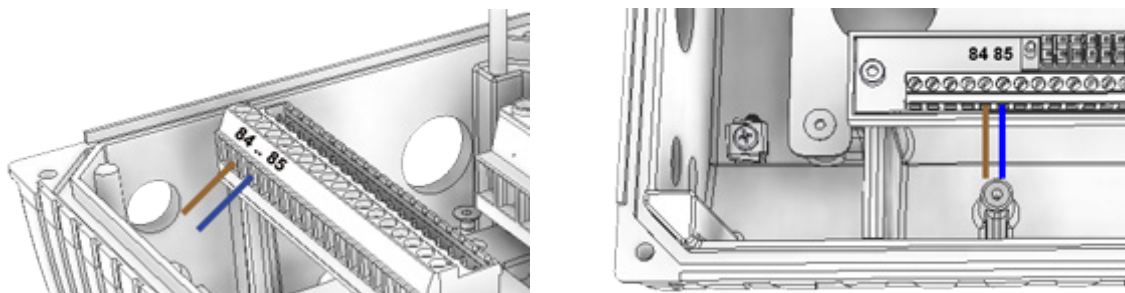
Anschlussklemmen AS-i, links Baugröße 1 – 3, rechts Baugröße 4
